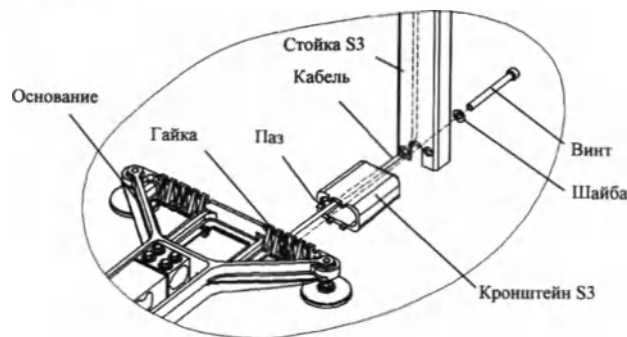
Крепление прямоугольной стойки к основанию платформы весовой
